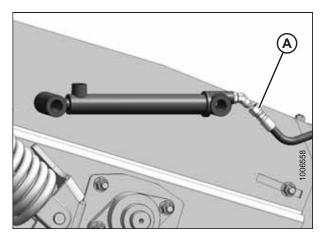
Cylindre asservi — Côté droit de la plateforme
